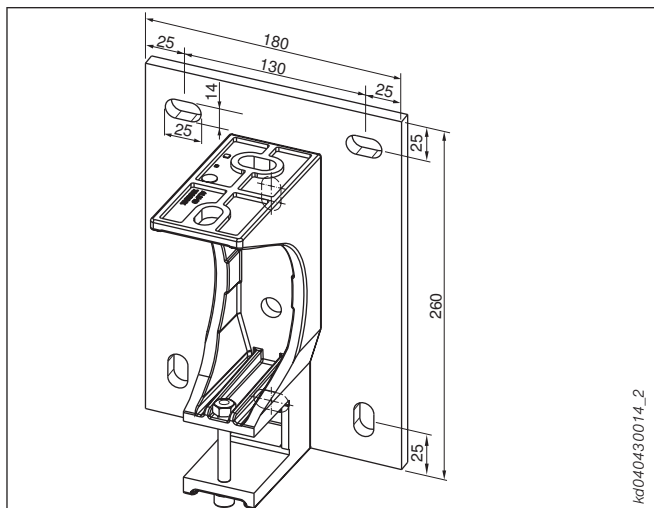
Consola tipo C – Fijación mural con placa de montaje pequeña
